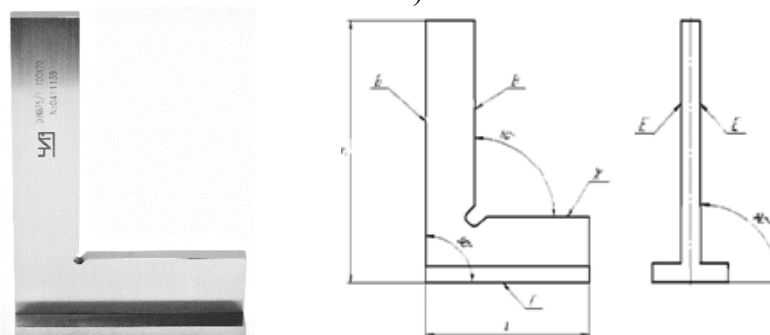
Общий вид угольников УП, обозначение основных размеров и поверхностей
